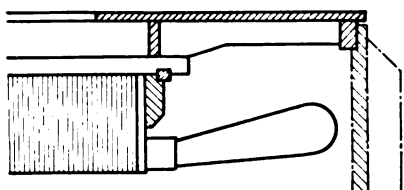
Lagerschildbefestigung beim geschweißten Walzstahlgehäuse.
